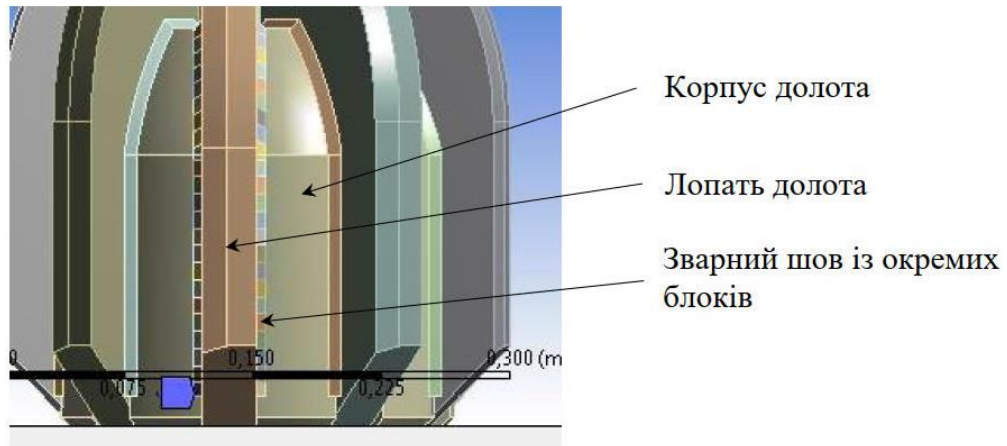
3D-модель зварного шва привареної лопаті до корпусу долота
